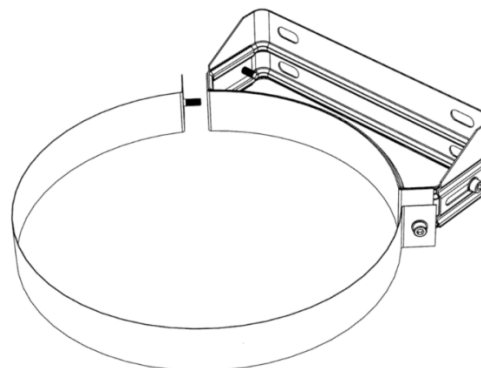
Collier mural réglable 50-75 mm (556)
